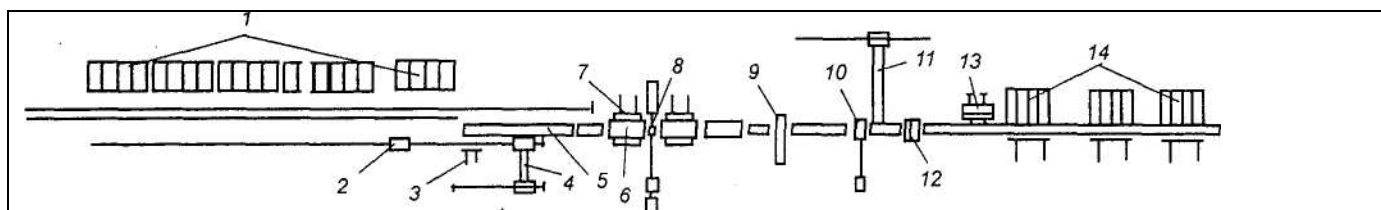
Схема расположения оборудования блюминга – слябинга 1500: 7 - нагревательные рекуперативные колодцы; 2 - слитковоз; 3 - сталкиватель слитков; 4 - устройство для смены слитковозов; 5 и 6 - приемные и рабочие рольганги; 7- манипулятор с кантователем; 8- рабочая клетка 1500; 9 - МОЗ; 10 - 16-МН ножницы; 11 - конвейер уборки обрезки; 12 - клеймитель; 13 - штабелер слитков; 14 - уборочные устройства для блюмов
